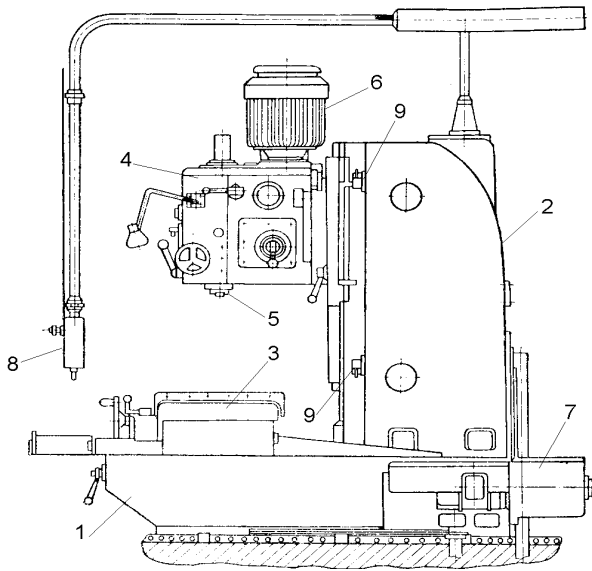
Зовнішній вигляд універсального вертикально-фрезерного верстату
